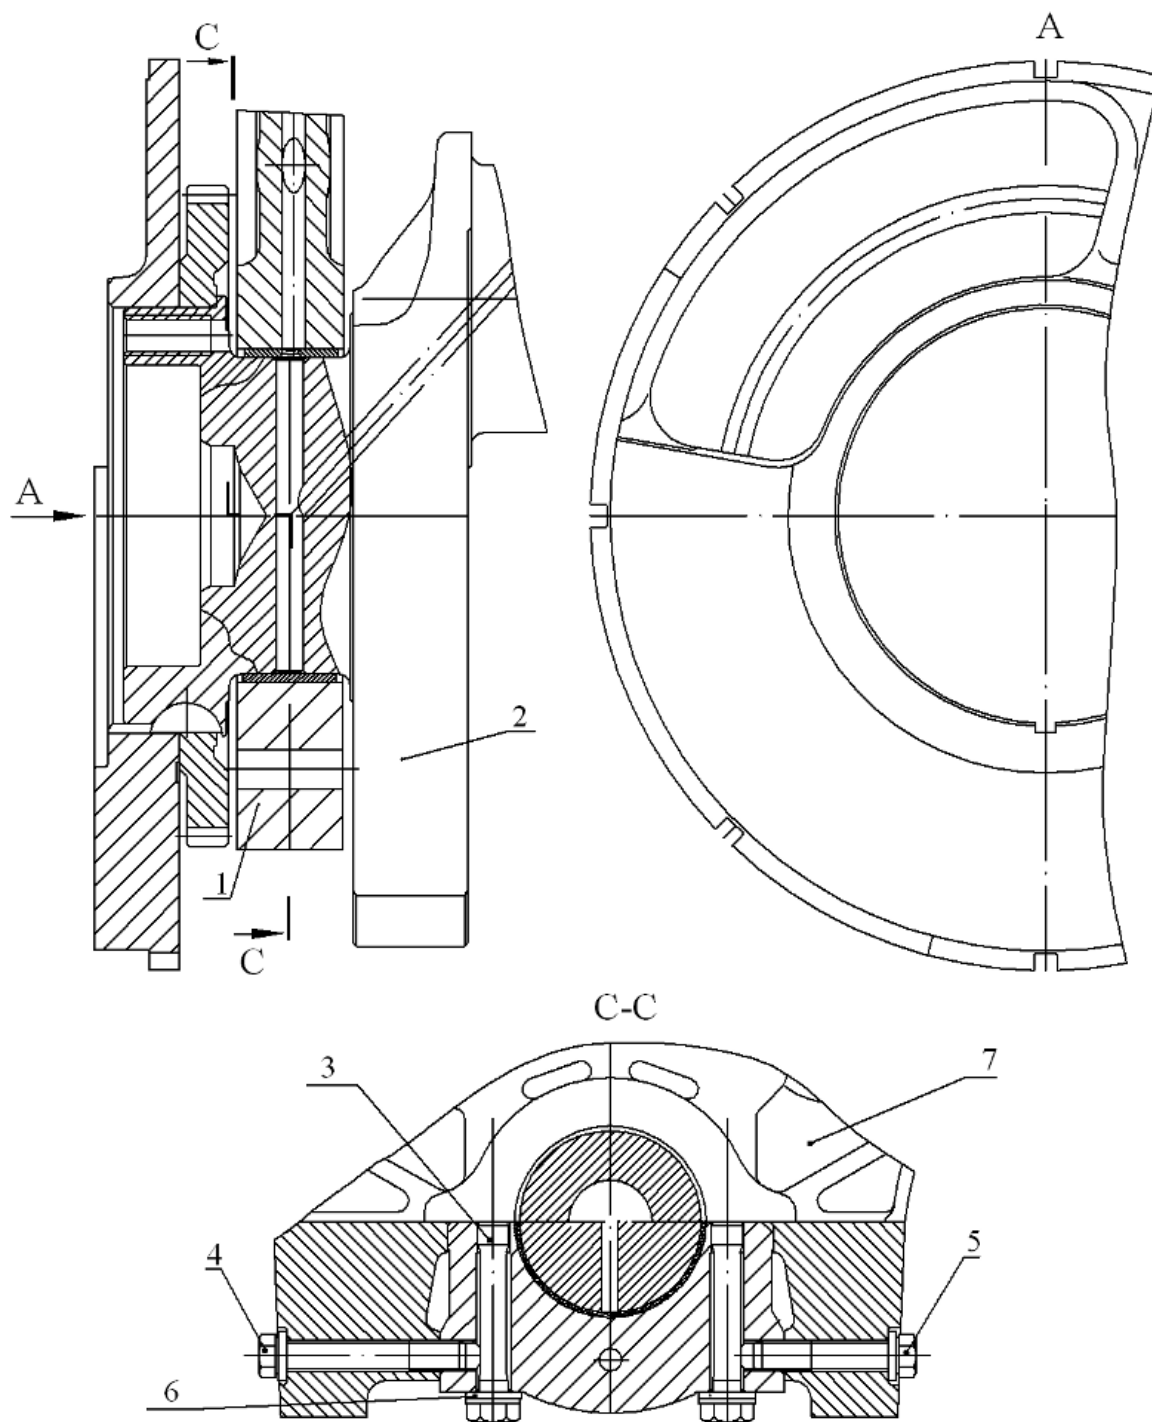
Установка крышек подшипников коленчатого вала:
